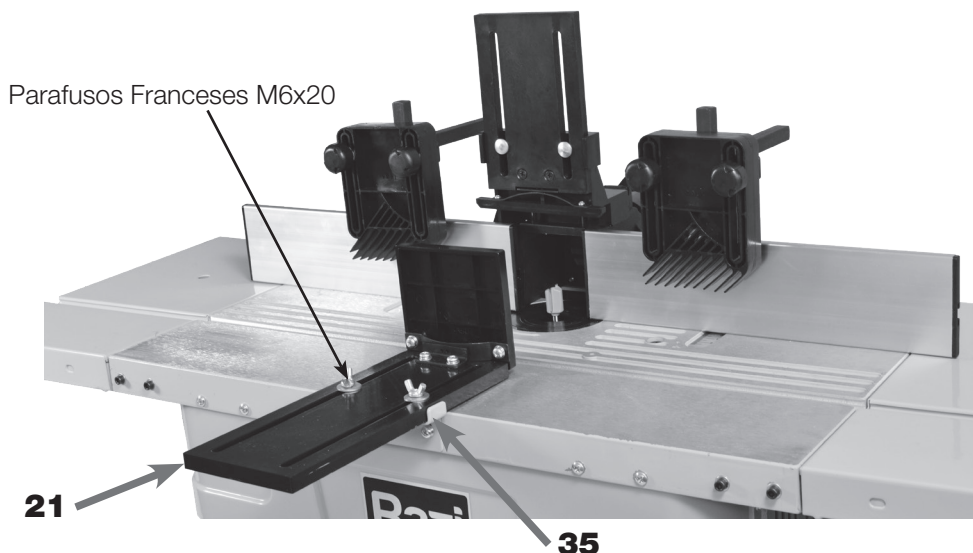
Montagem do Conjunto da Barra de Pressão Frontal
